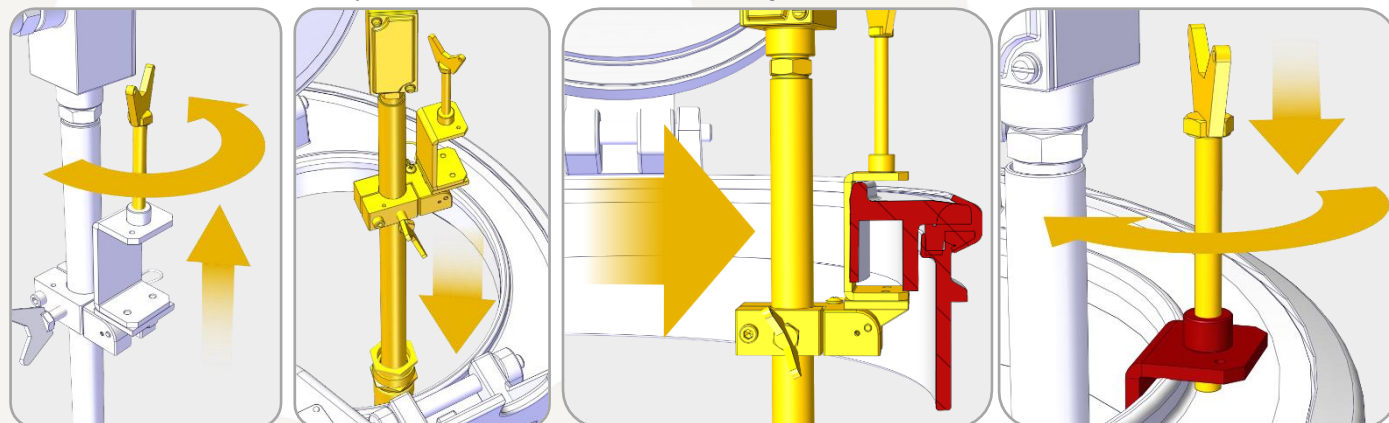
Fixação do Suporte em Acesso COM Bocal de Visita
